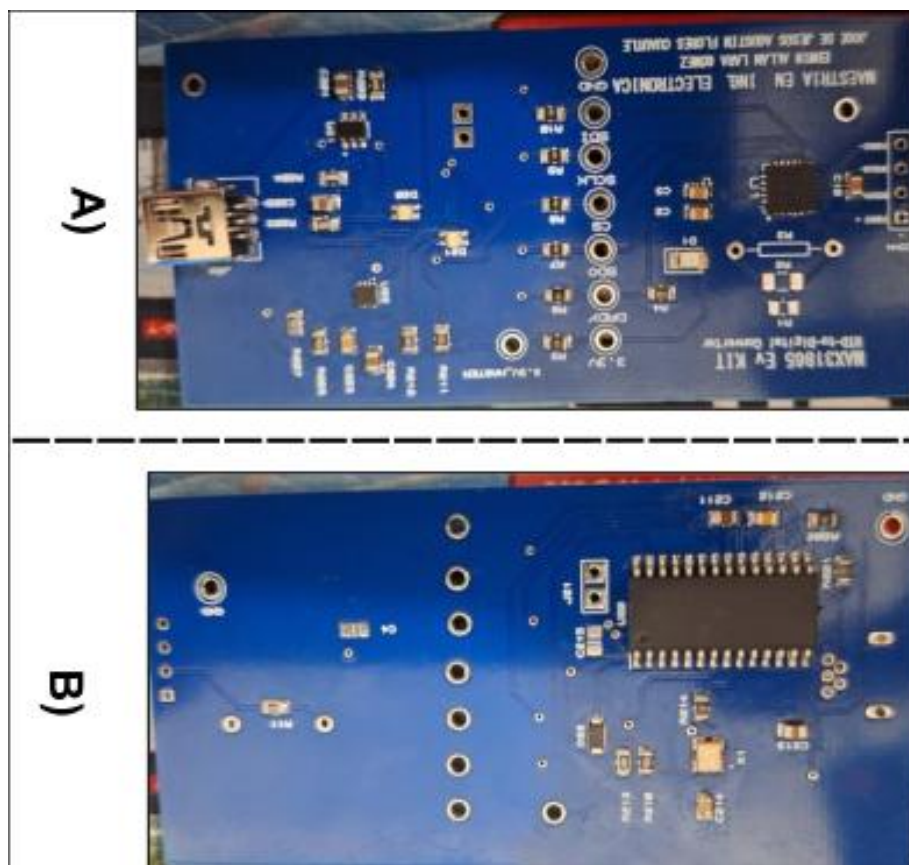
A) Vista superior y B) vista inferior del MAX31865EVKIT con componentes ensamblados.
